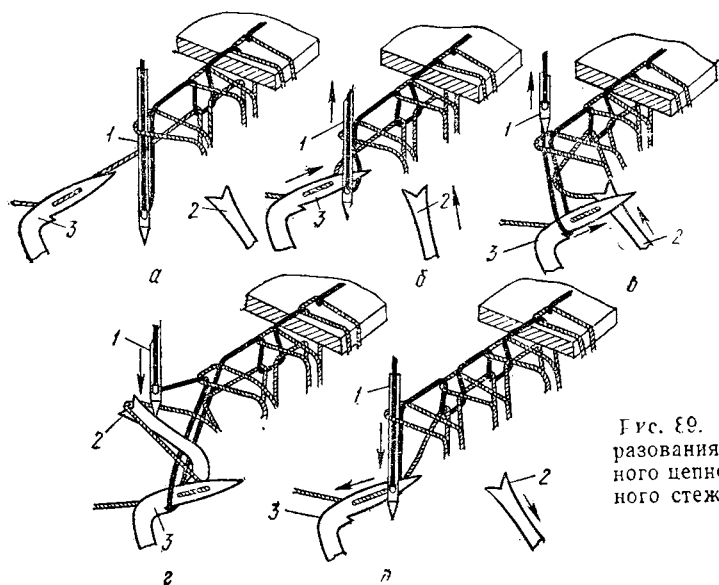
Процесс образования двухниточного цепного обметочного стежка
